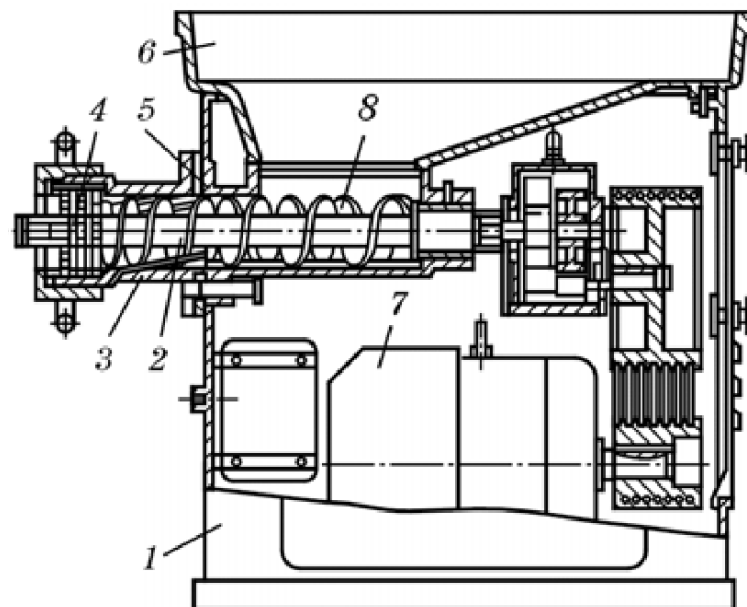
М'ясорубка типу «вовчок» з примусовою подачею сировини: 1 – основа; 2 – шнек основний; 3 – циліндричний корпус шнека; 4 – механізм подрібнювальний; 5 – корпус; 6 – зона приймача; 7 – електродвигун приводу; 8 – спіральний додатковий шнек. [10]
